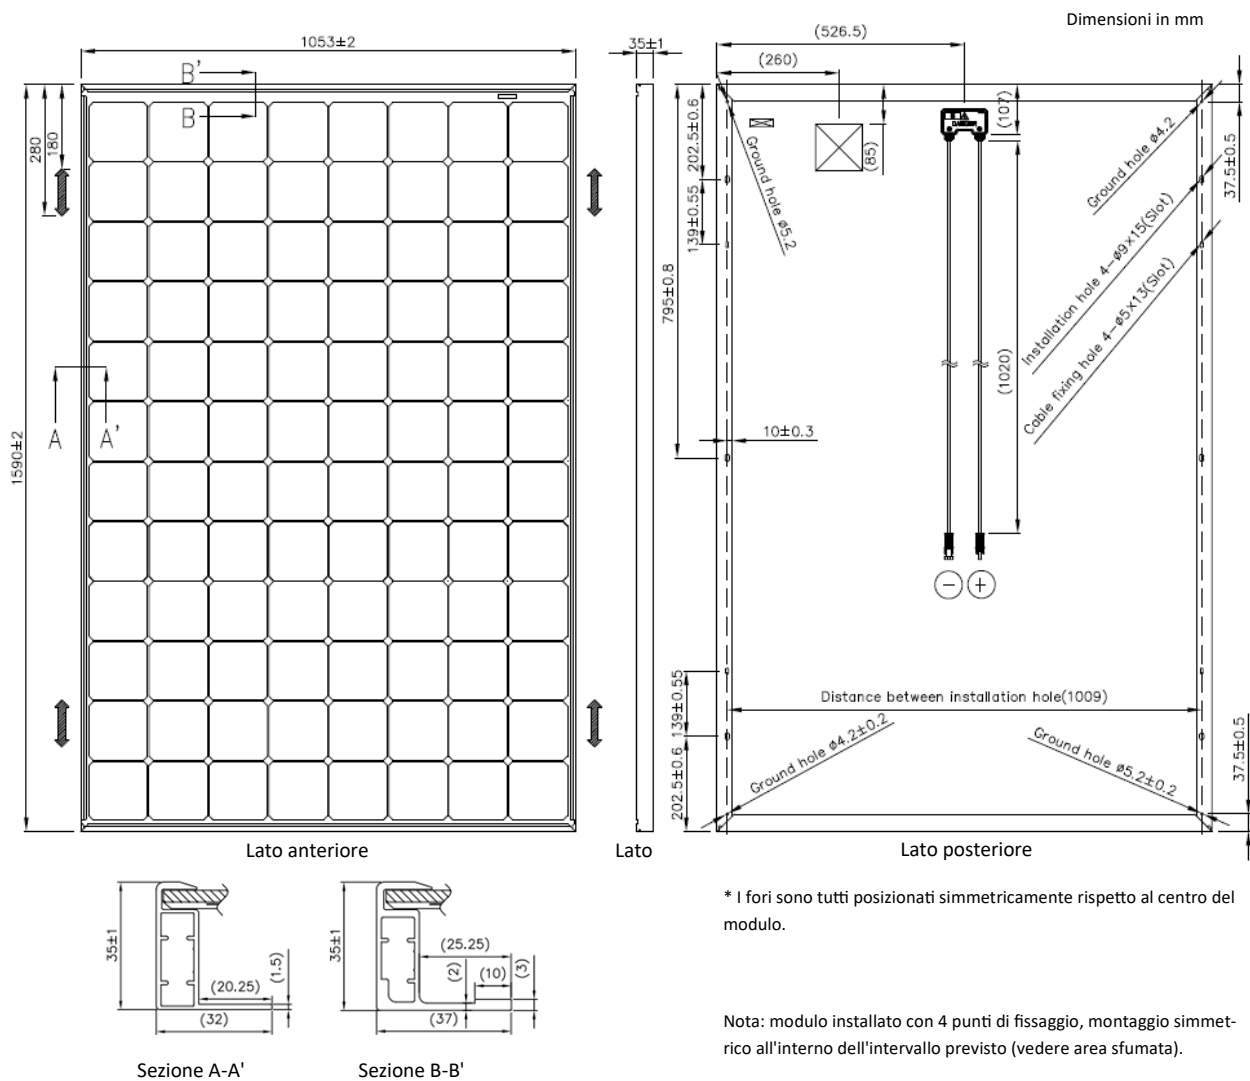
Dimensioni del modulo (VBHNxxxSJ47)
